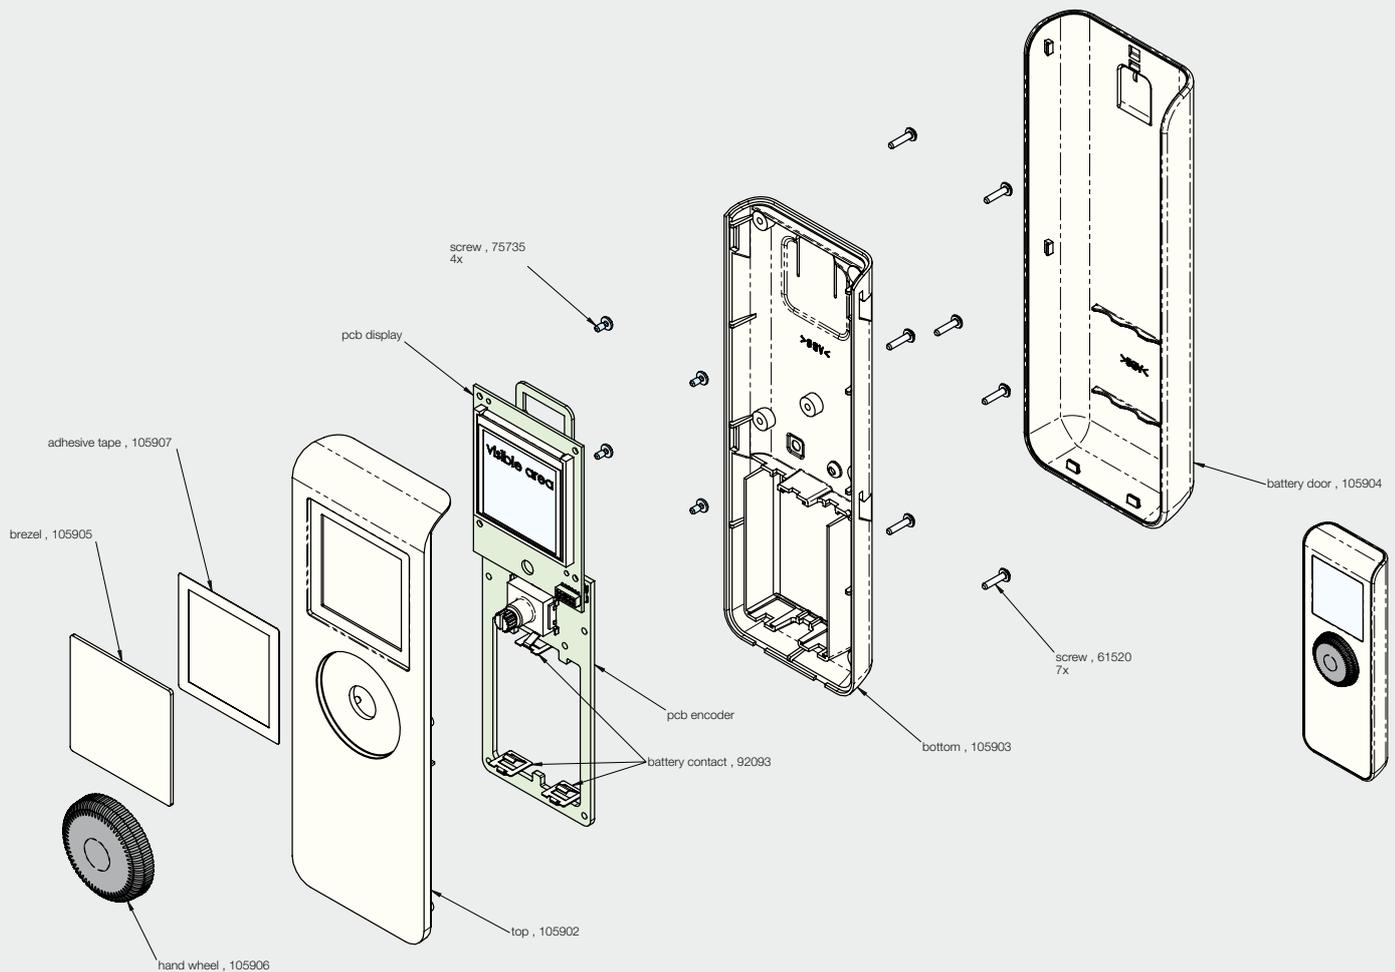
Die Explosionszeichnung der FS20 DF zeigt den mechanischen Aufbau des Gerätes.
